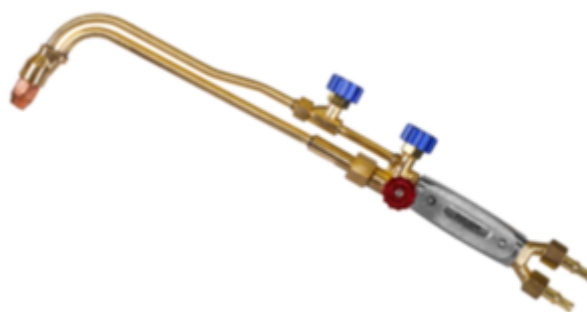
Резак пропановый Сварог РЗП-02М [21]
